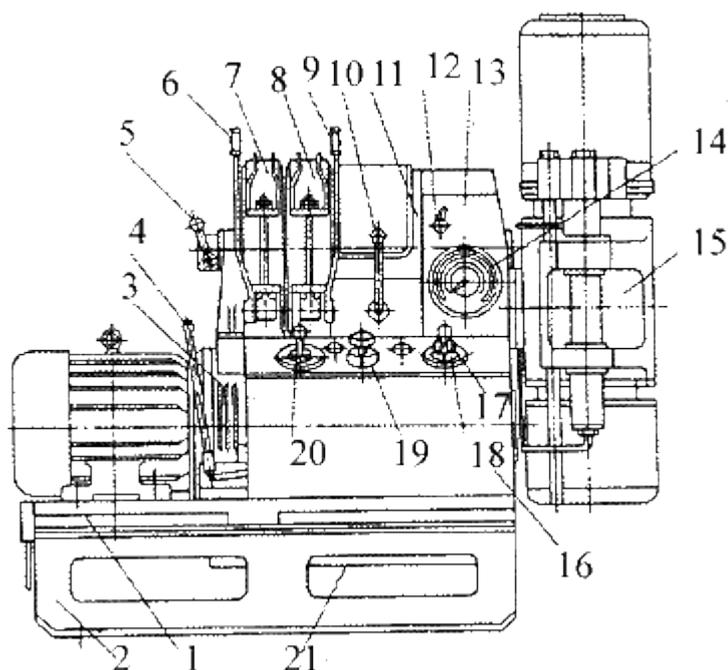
Буровой станок СКБ-4: 1 – станина; 2 – рама; 3 – сцепление; 4 – рукоятка сцепления; 5 – рукоятка включения лебедки; 6, 9 – рычаги тормозов подъема и спуска; 7, 8 – тормоза подъема и спуска; 10 – рычаг коробки передач; 11 – лебедка; 12 – рукоятка раздаточной коробки; 13 – трансмиссия; 14 – указатель давления; 15 – вращатель; 16 – гидросистема станка с автоперехватом; 17 – дроссель; 18 – прибор управления; 19 – регулятор подачи; 20 – распределитель; 21 – цилиндр перемещения станка.
